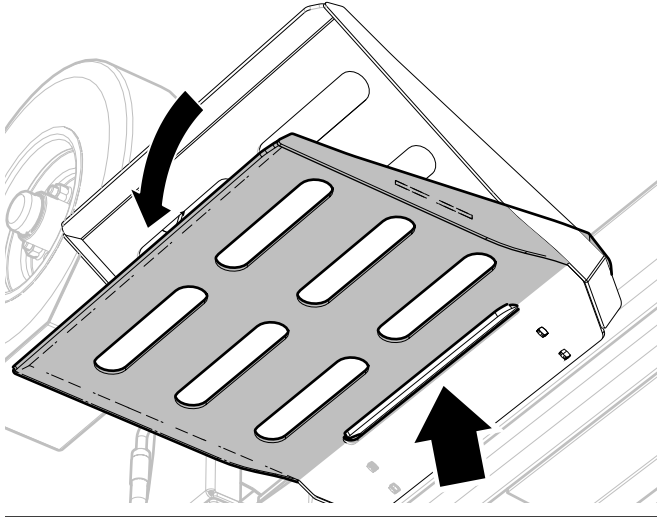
Glissez le plateau sur l'aile de la fenduse
